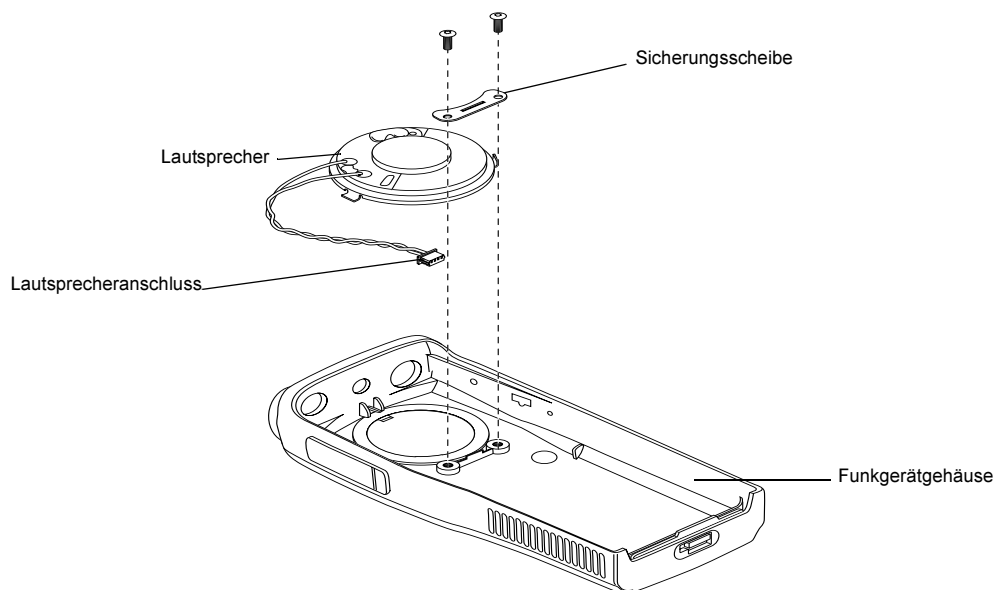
Entfernen der Lautsprecher-Mikrofon-Baugruppe
